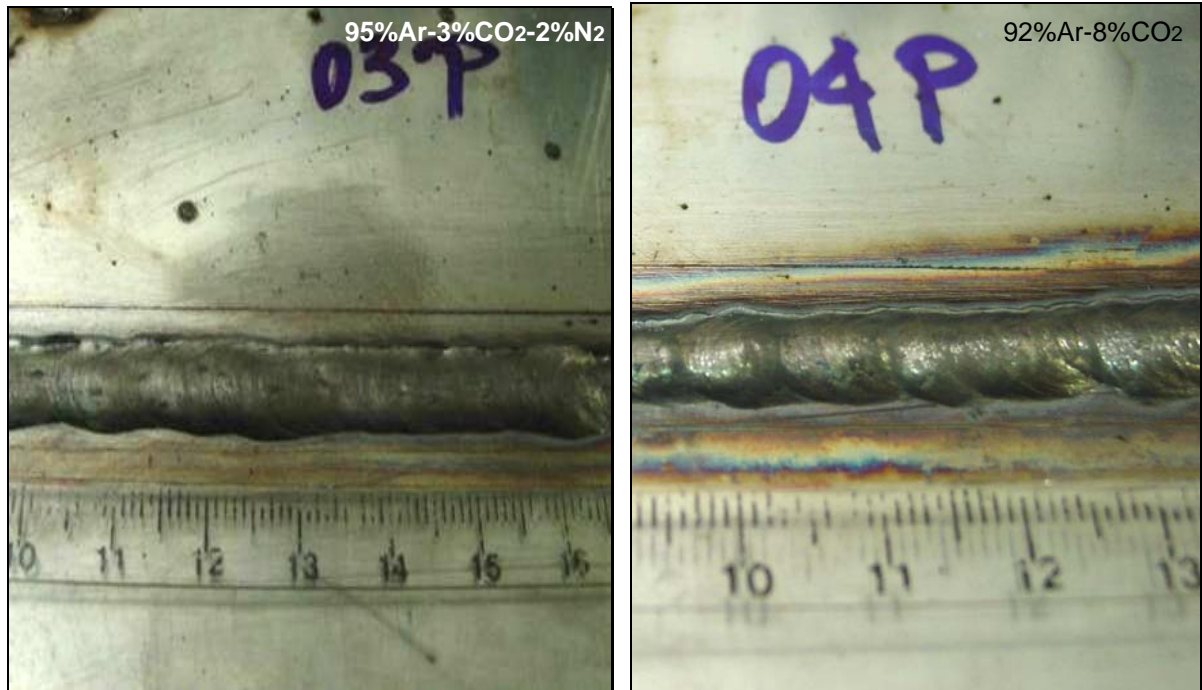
Aspecto do cordão de solda – MAG-P com comprimento do eletrodo de 15 mm
